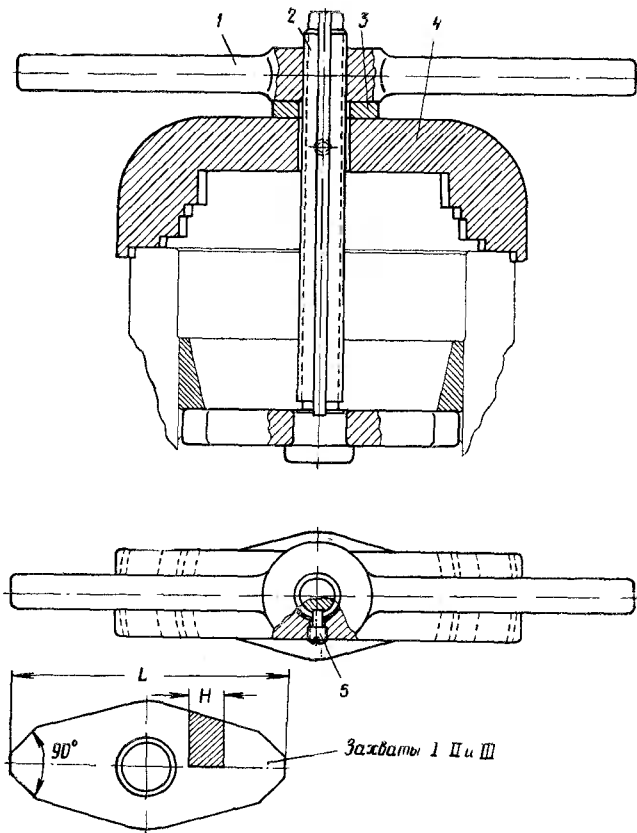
Съемник наружных колец подшипников ступиц колес:
